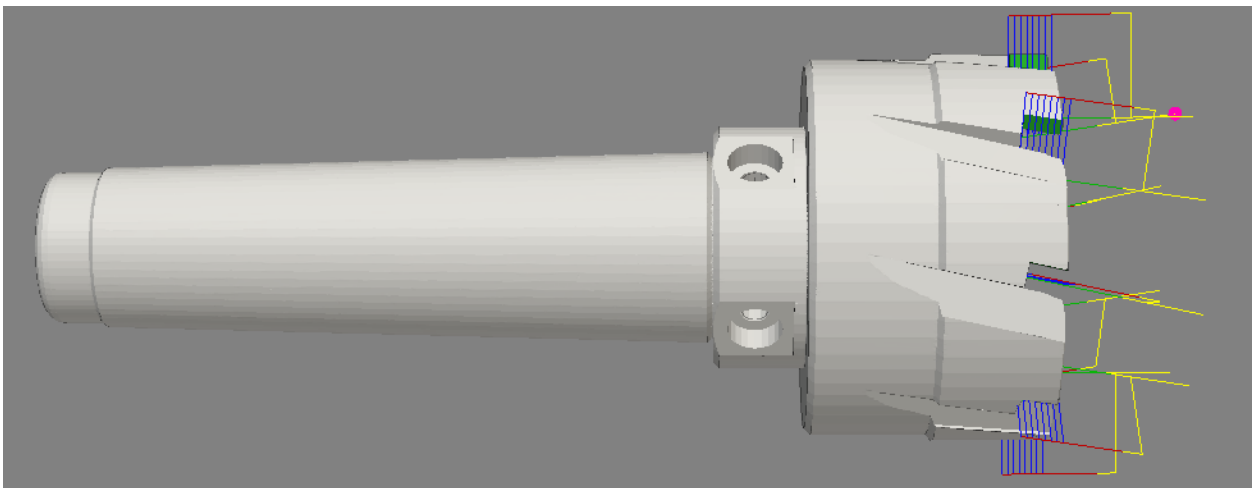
Фрезерування посадкових місць під пластинки
